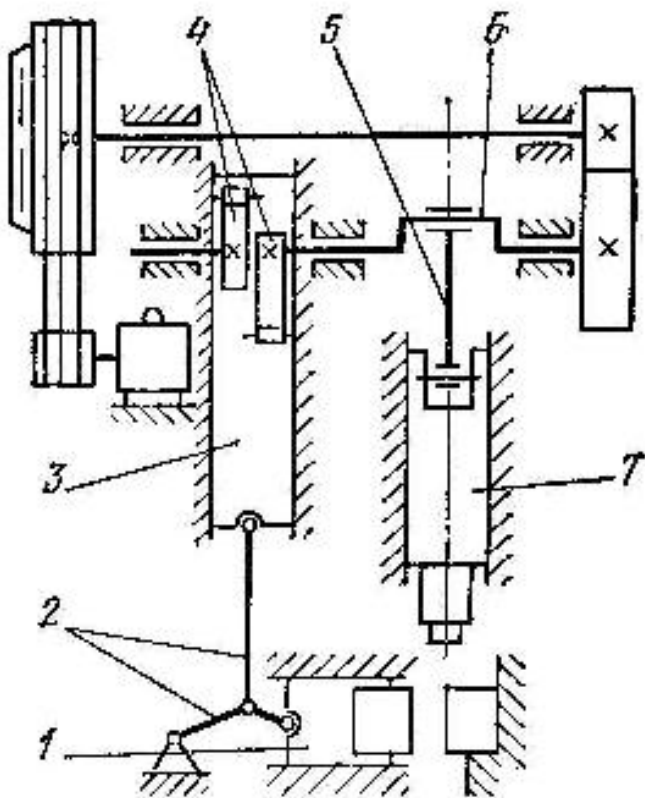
Кинематическая схема горизонтально-ковочной машины
